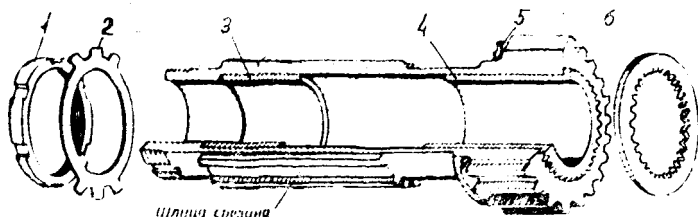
Валик крыльчатки нагнетателя: 1—гайка; 2—замок гайки; 3—передняя втулка; 4—задняя втулка; 5—бронзовая шайба; 6—шлицевая шайба
